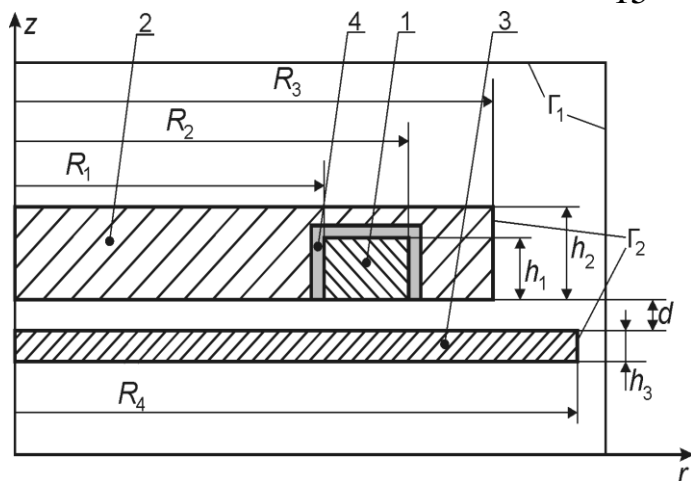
Розрахункова схема індуктора разом із заготовкою: 1 – струмопровід; 2 – допоміжний екран; 3 – заготовка; 4 – ізоляція струмопроводу
